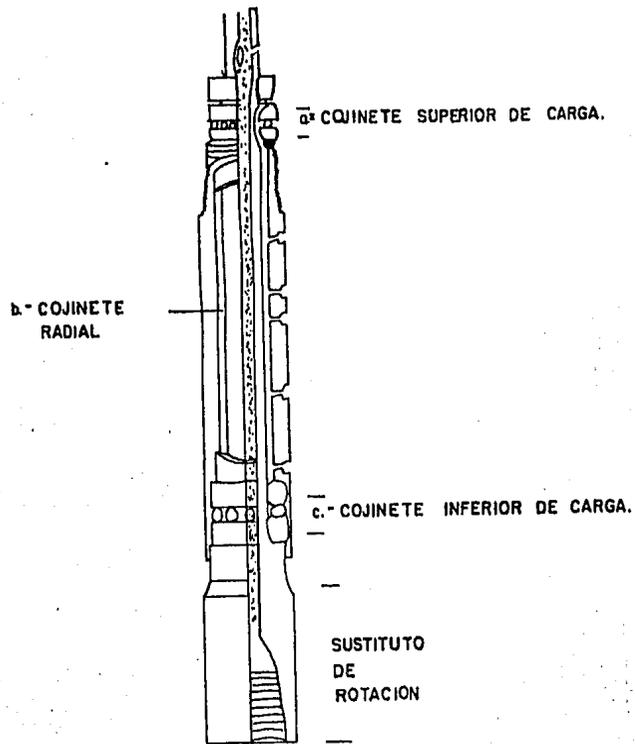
ENSAMBLE DEL COJINETE Y LA FLECHA MOTRIZ.
